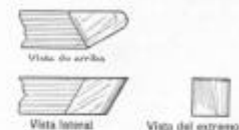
Detalle de la cuchilla para tornearse en la izquierda
